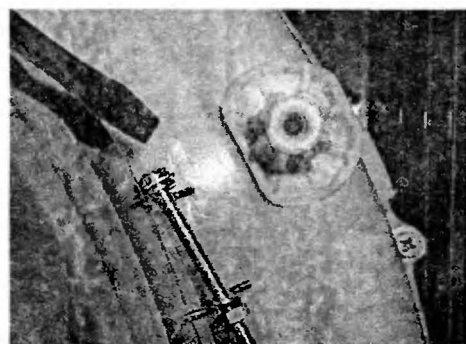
Расположение винта, стягивающего крепежный хомут уплотнителя люка
